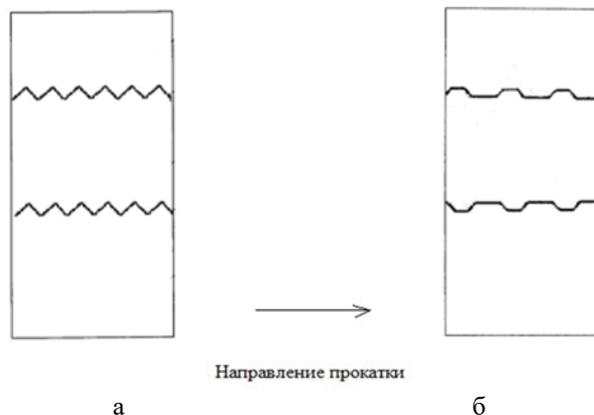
Виды формируемого рельефа: а – зубчатый рельеф; б – трапециевидный рельеф
